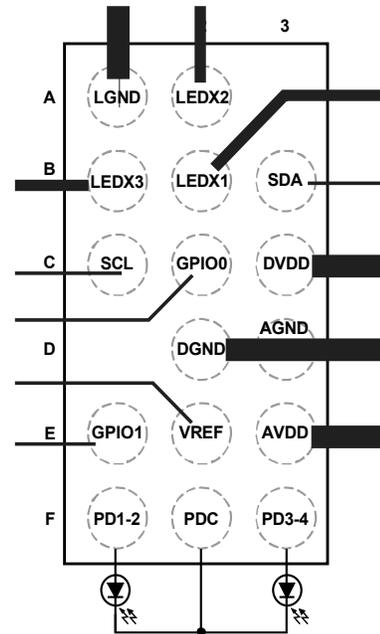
ADPD105 连接和 PCB 布局图 (顶视图)
